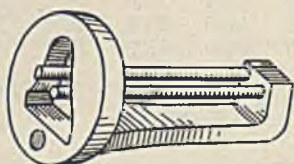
Schlauchmaschinenkapsel für Innendrähte
